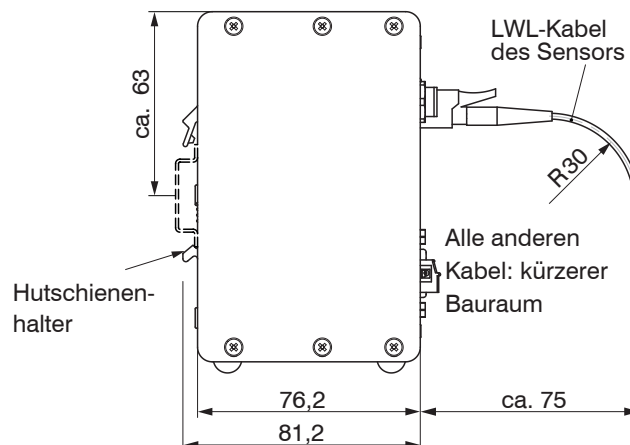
Maßzeichnung Seitenansicht des Controllers IFC2421/2422/2465/2466, Abmessungen in mm
